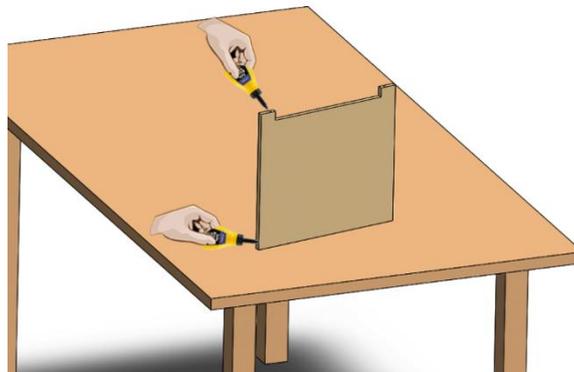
Paso 13 del ensamblaje del cajón (conjunto 2)
